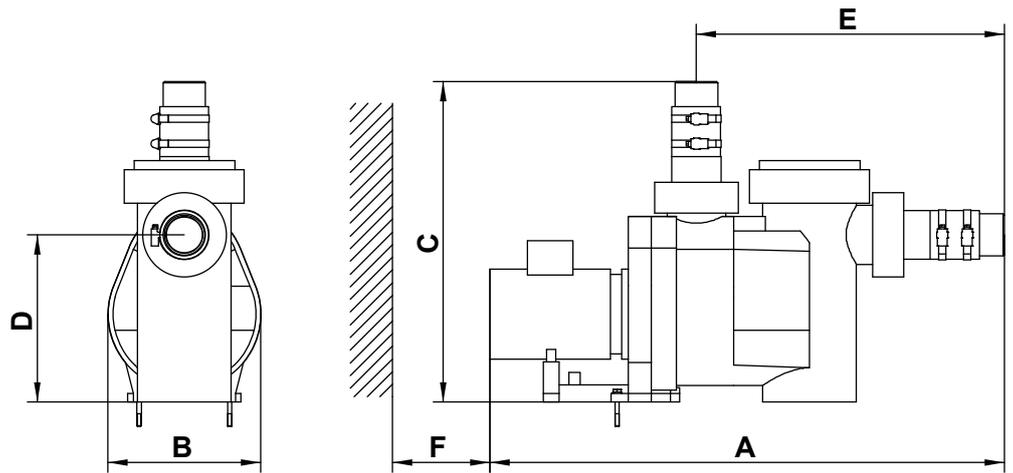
Maßzeichnung Umwälzpumpen Prime
